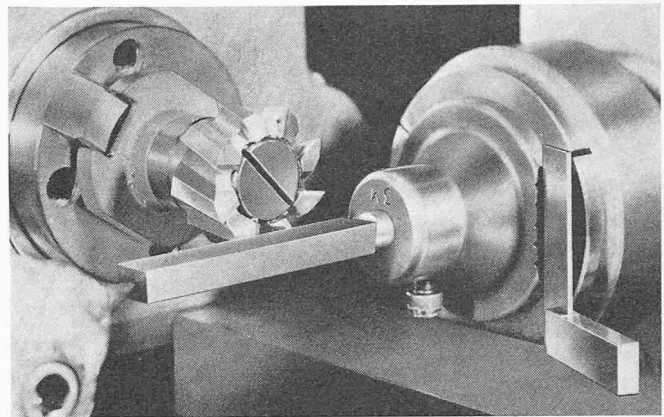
Bearbeitung einer Elektrode in einem Elektrodenhalter
